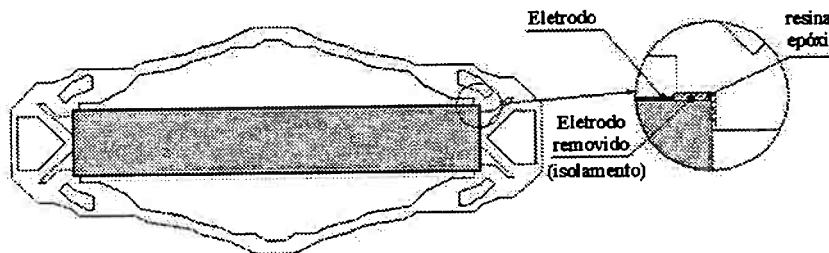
Detalhe da conexão entre as piezocerâmicas e as estruturas acopladas.
